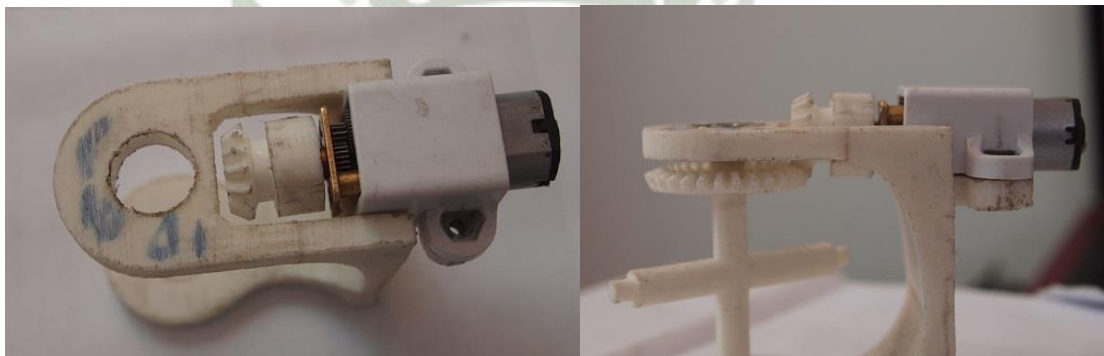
29 Ensamblaje de la muñeca con engranajes cónicos
